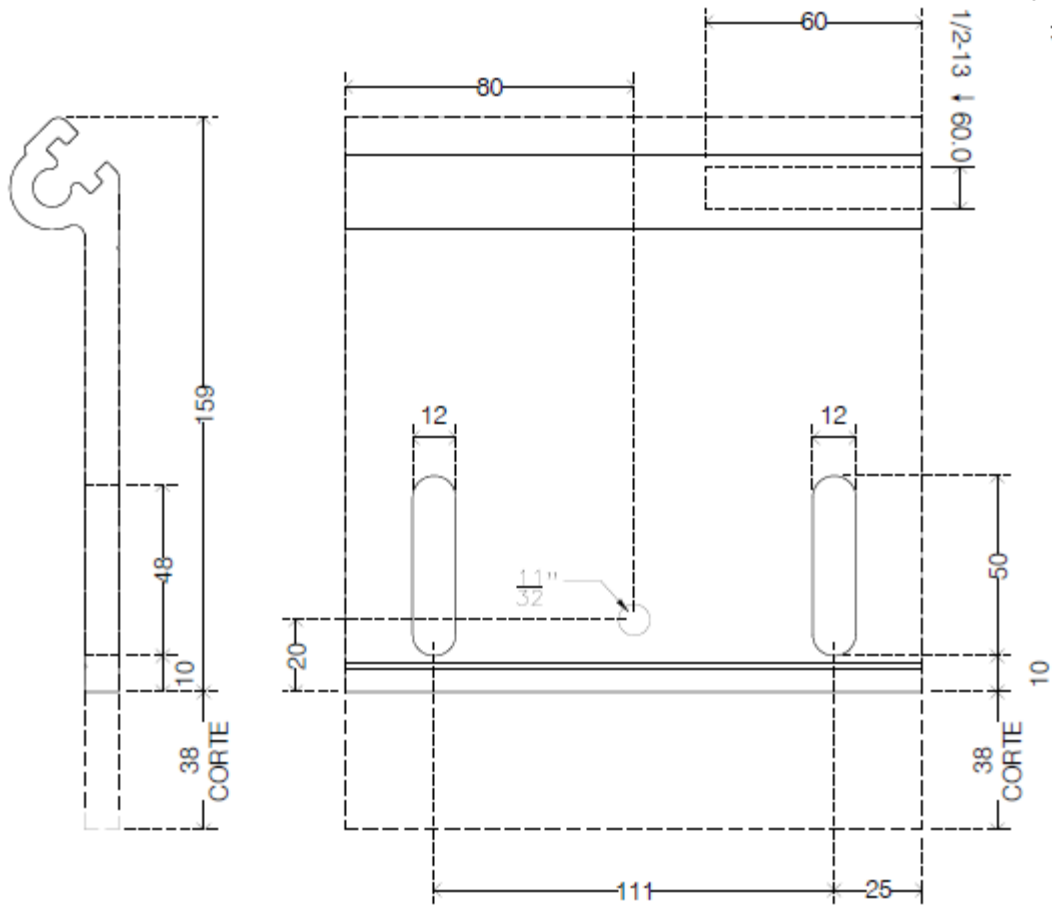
Detalle ancla hembra esquinas perfil 69173. Fuente: Aluvisa (2019)
